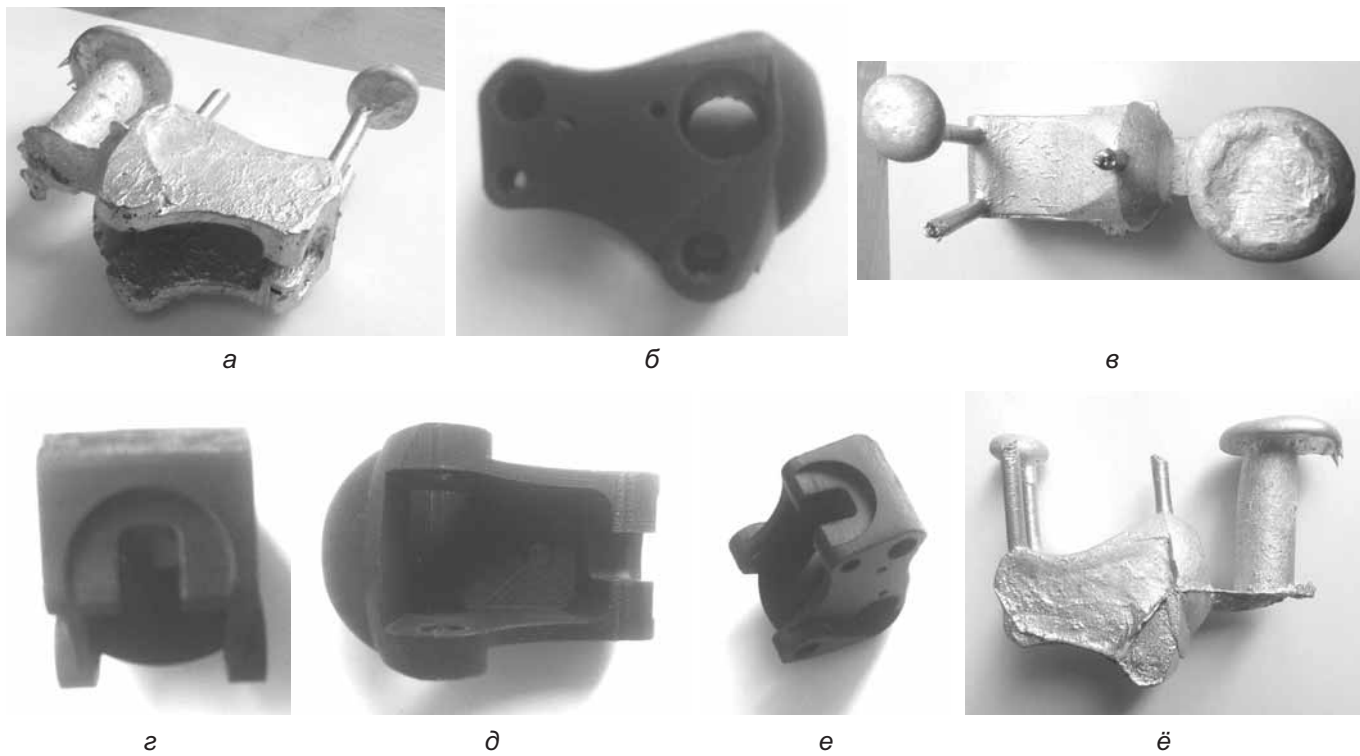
Модели и отливки «нижний шарнир» (а-ж)
